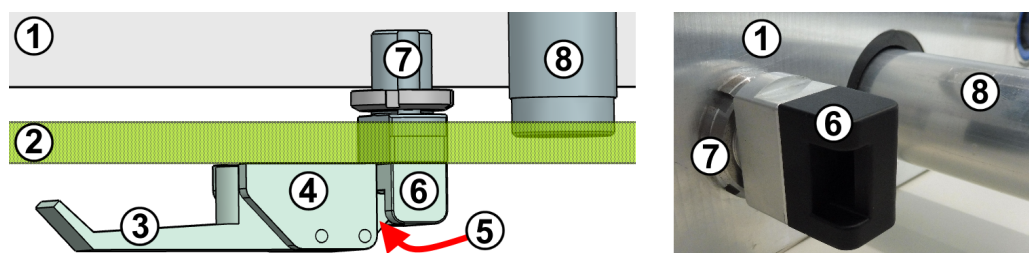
Компрессионный замок, вид сверху (слева) и подробное изображение (справа)
